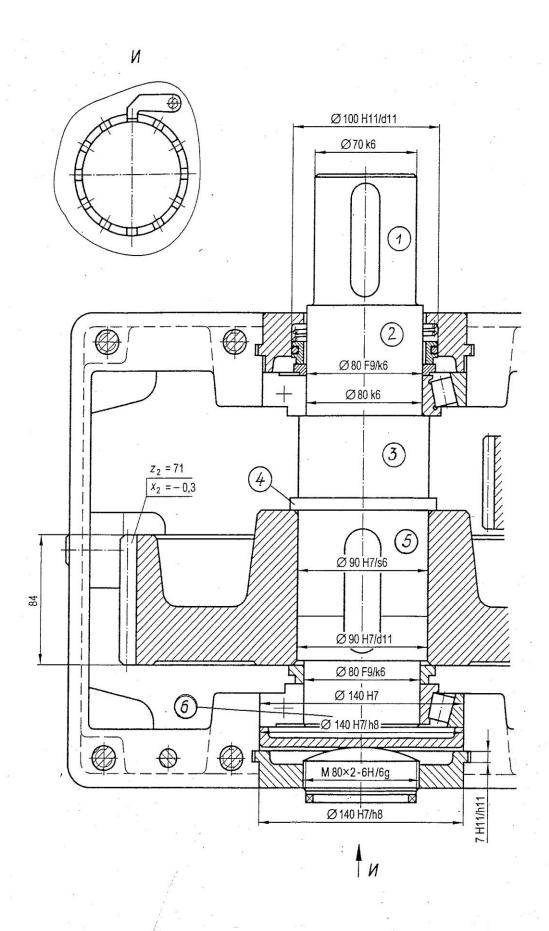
Тихоходный вал редуктора с цилиндрическим концом и закрепленным одним насадным цилиндрическим зубчатым колесом тихоходной ступени [I] (к примеру 2.1)
